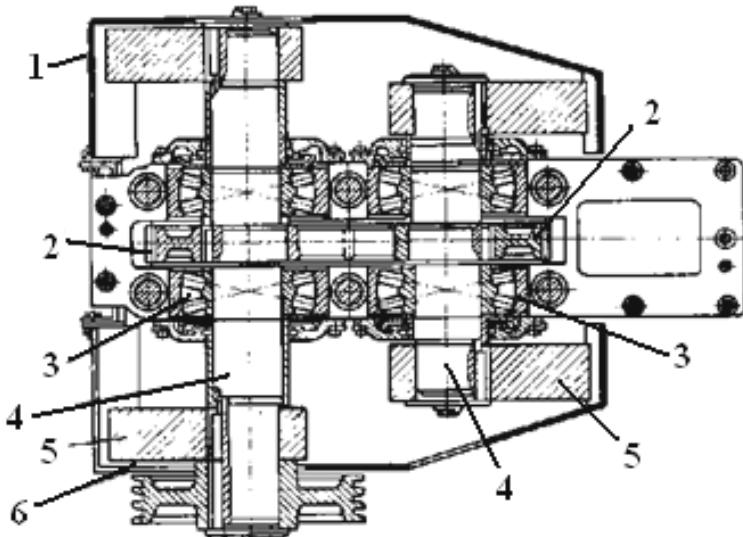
Вибратор самобалансный грохota ГСЛ
